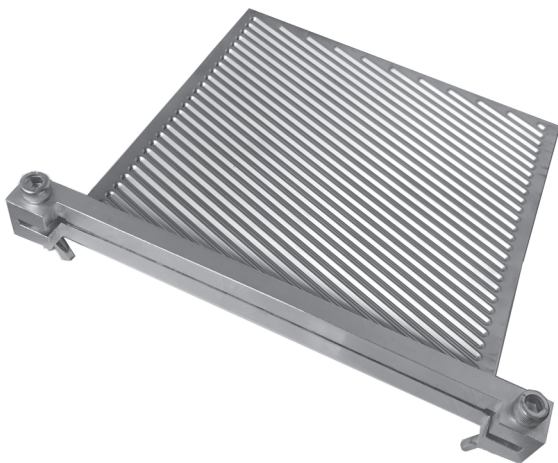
Приспособление для прижима свариваемых кромок
